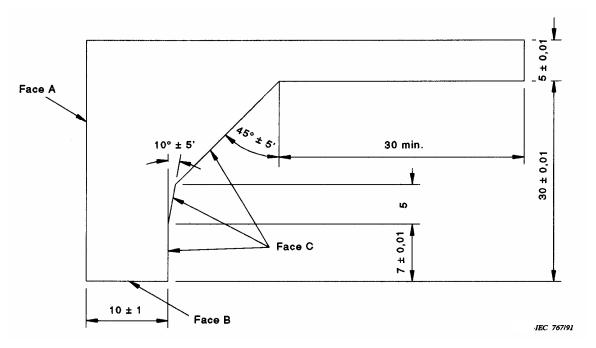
Disposition pour l'essai des plaques de recouvrement
